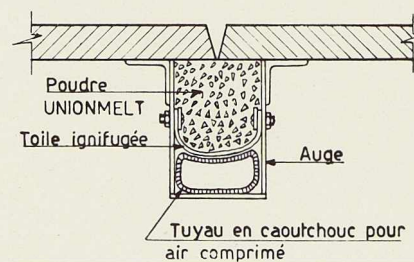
Exécution de la soudure longitudinale du tube.
